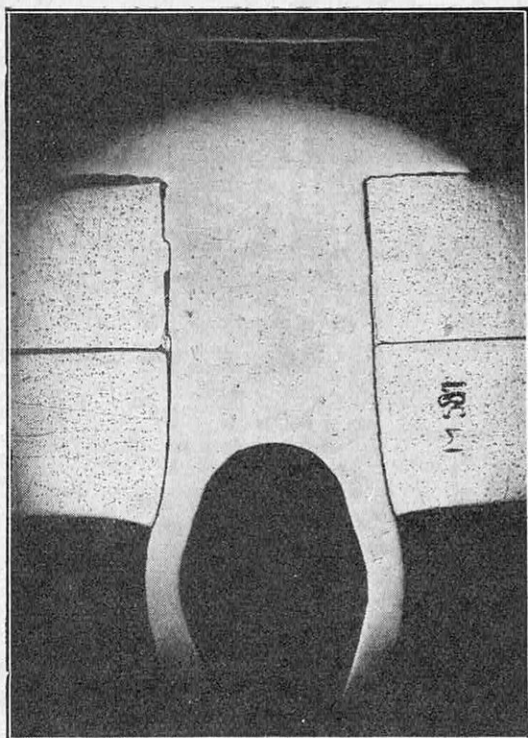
COUPE D'UN RIVET MONTRANT L'ÉVASEMENT PRODUIT PAR L'EXPLOSION DE LA CHARGE PLACÉE DANS LA TIGE DU RIVET
